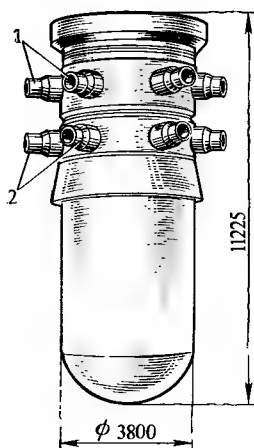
Внешний вид корпуса водоводяного реактора:
